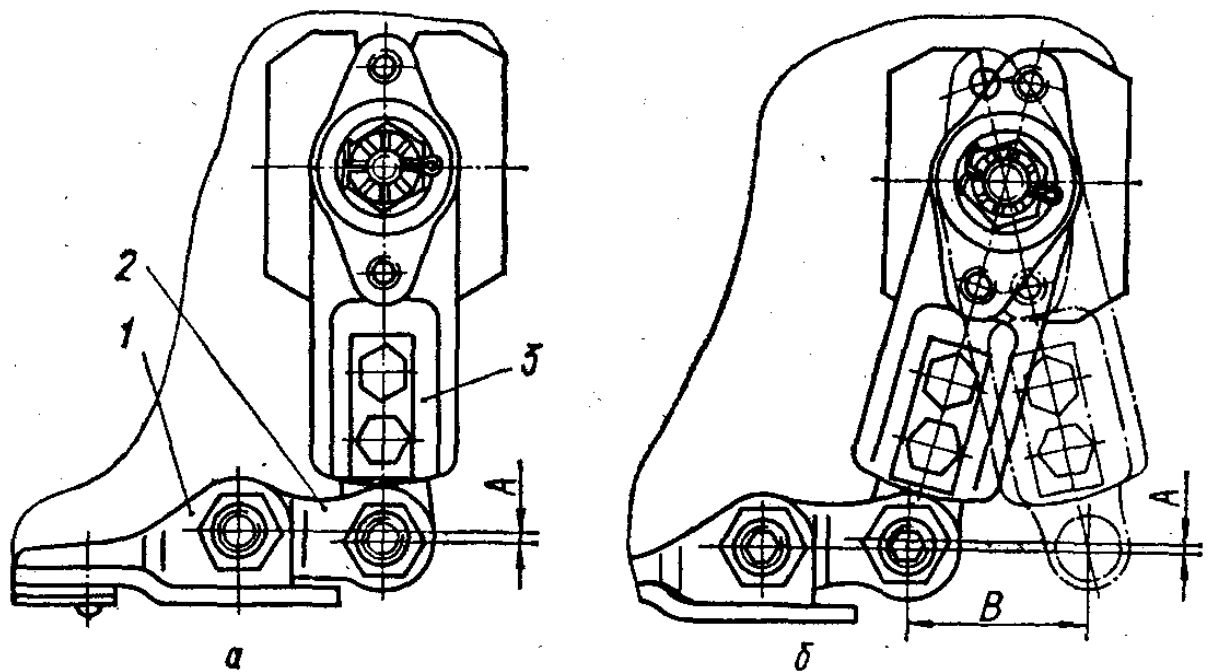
Регулювання з'єднання головки ножа і головки важеля механізму коливальної шайби:
